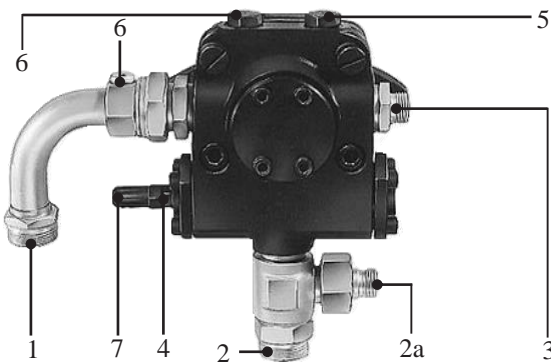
Насос шестеренчатый жидкотопливный марки ТА2
